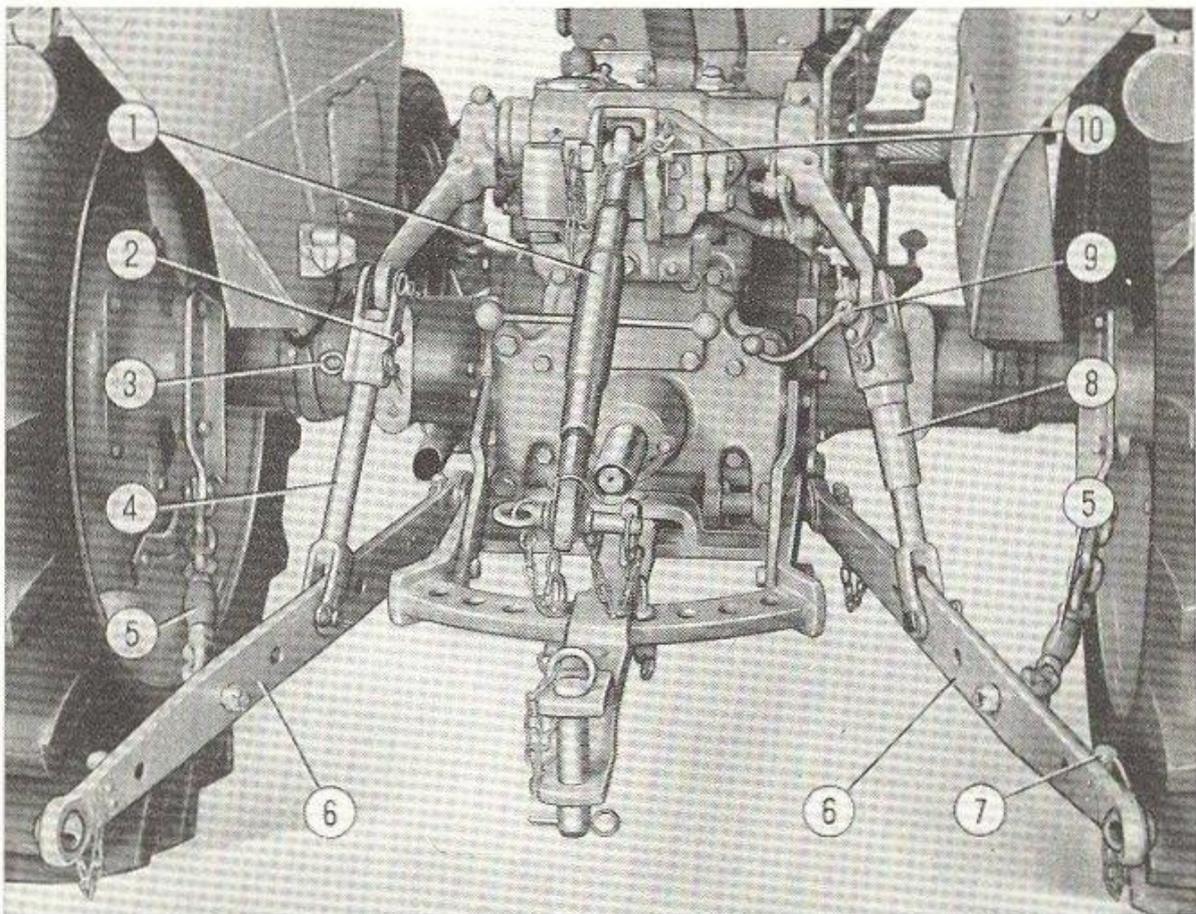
Porte-outils du dispositif de relevage hydraulique.
